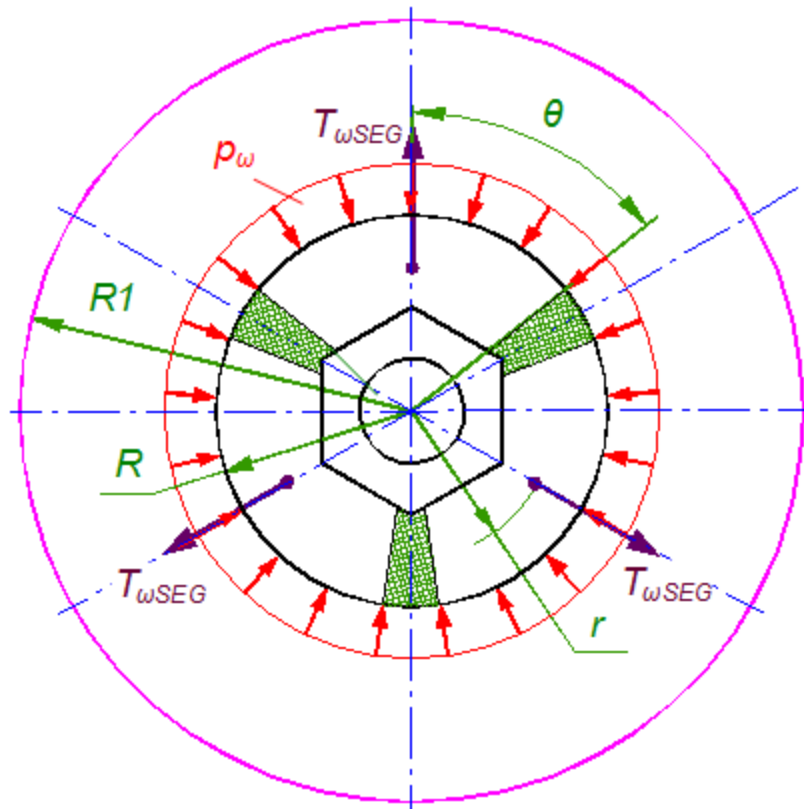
Розрахункова схема контакту сегментів розтискної цанги із внутрішньою поверхнею заготовки при усталеному обертанні (без врахування статичної сили затиску)
